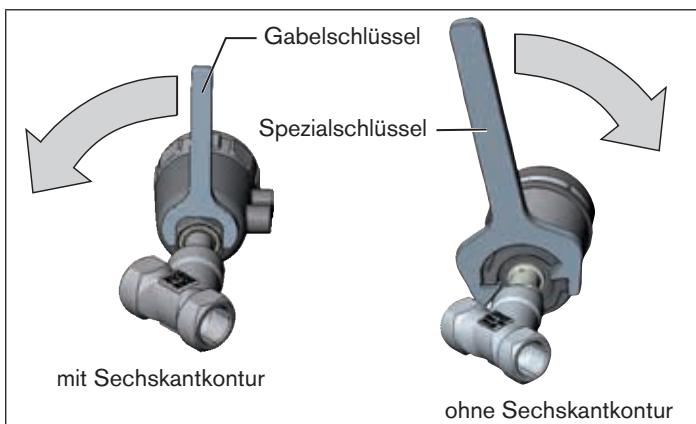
Drehen mit Spezialschlüssel / Gabelschlüssel
